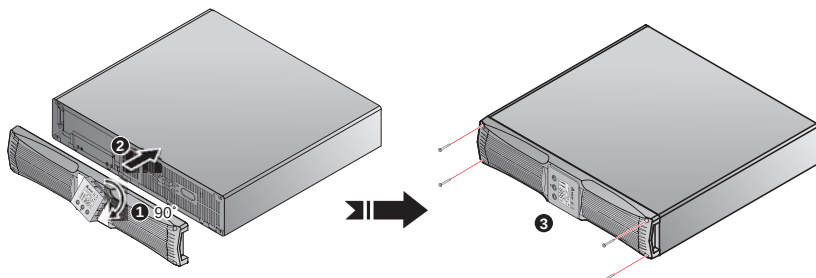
Demontaż plastikowego panelu przedniego)
